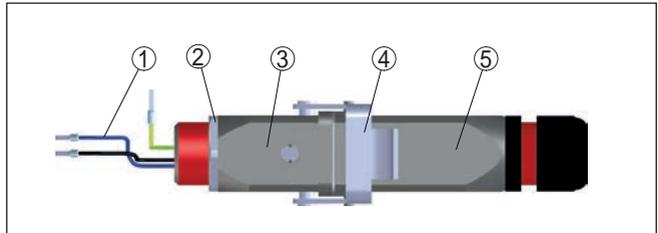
Aufbau Steckverbinder Harting HAN 8D - Beispiel gerade Ausführung
